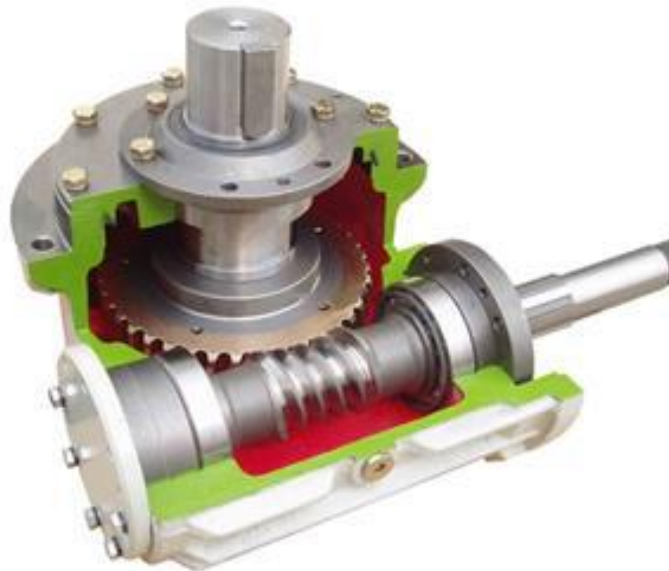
Червячный редуктор с вертикальным валом червячного колеса
